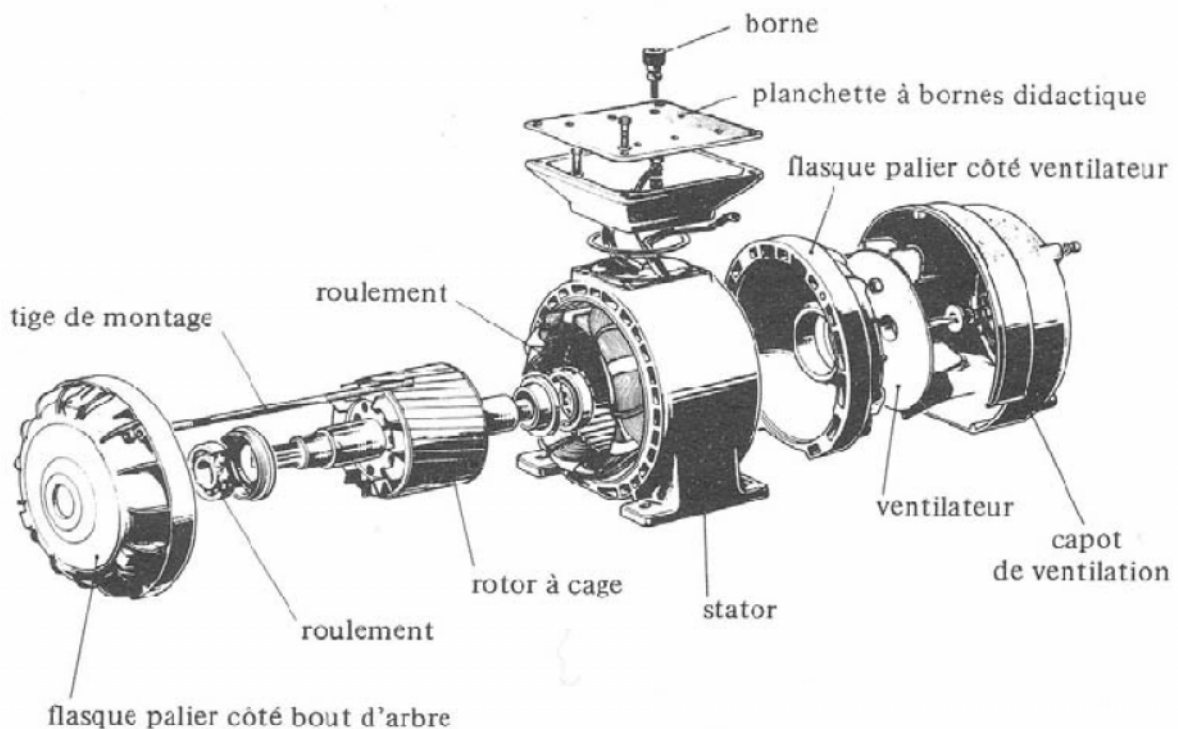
Vue éclatée d'une machine asynchrone triphasée à cage.
